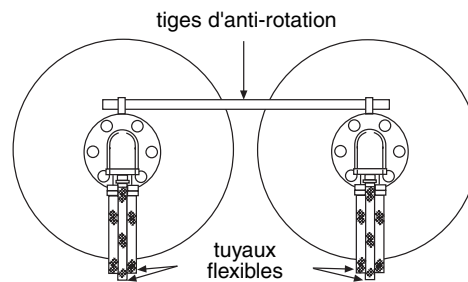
Installation horizontale des tiges dans les oreilles situées sur le corps.
